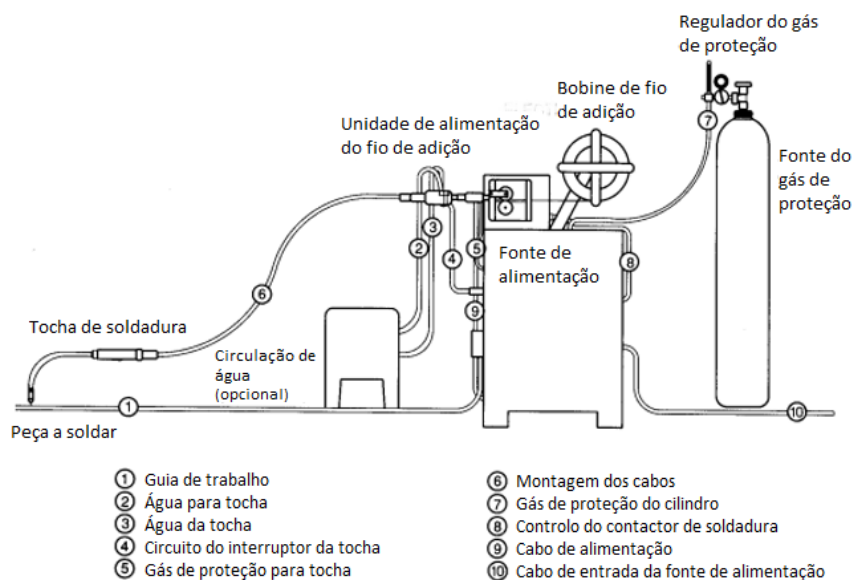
Esquema representativo de uma configuração semiautomática de soldadura MAG (Adaptado de: O'Brien, 2004)
